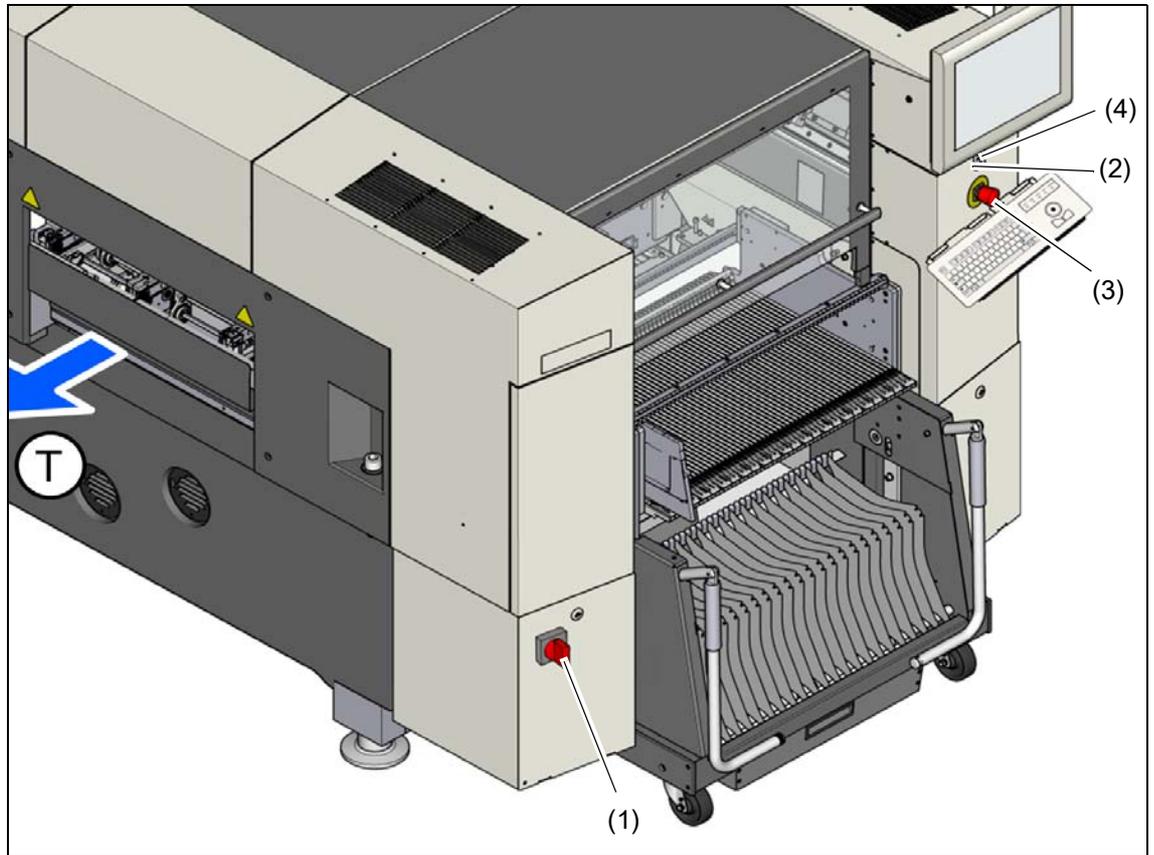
开关和按钮的位置 - 从 PCB 输出侧观察
